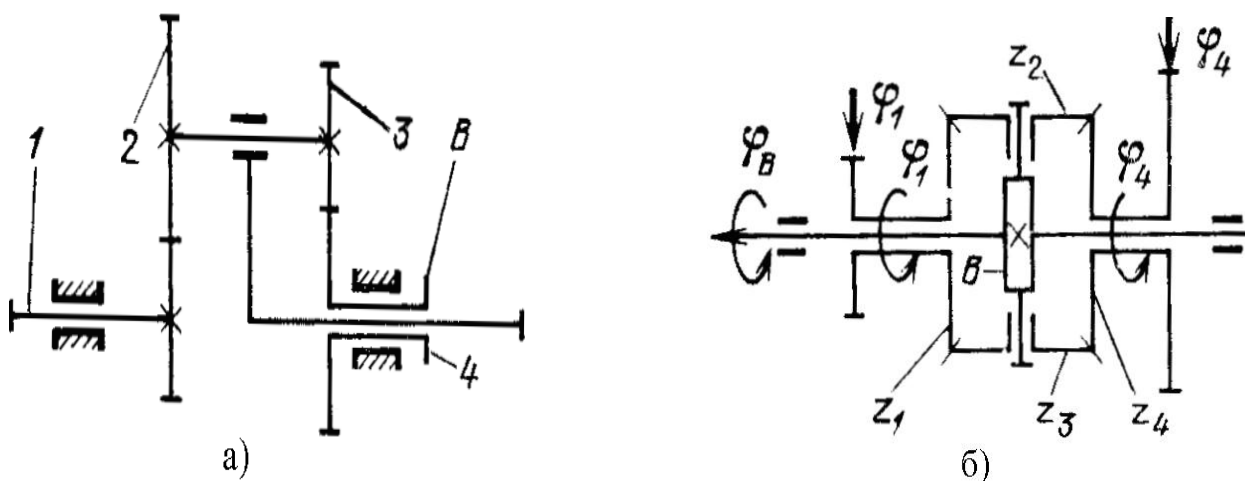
Четырехступенчатый планетарный редуктор
